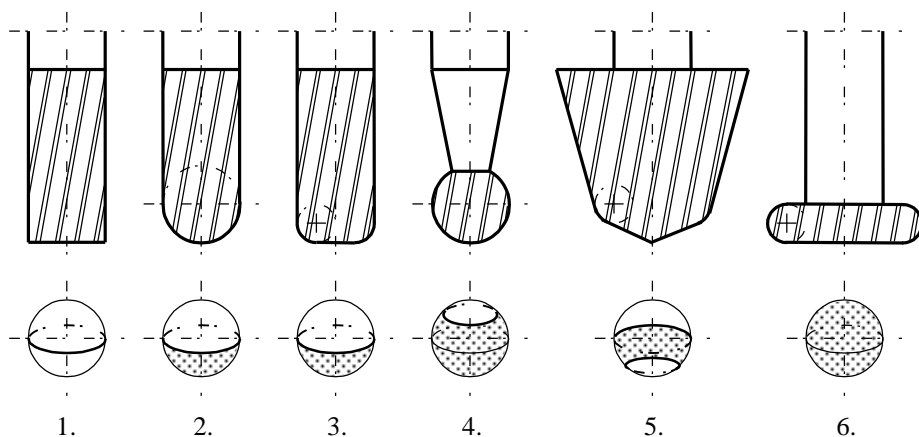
Примеры отображений Гаусса и сферических индикатрис исходных инструментальных поверхностей универсальных инструментов для обработки сложных поверхностей деталей.
